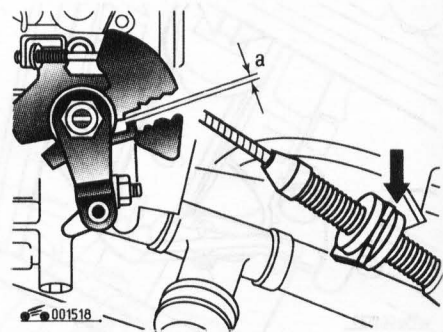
Регулировка троса привода дроссельной заслонки на двигателях SOHC (с механической коробкой передач)
